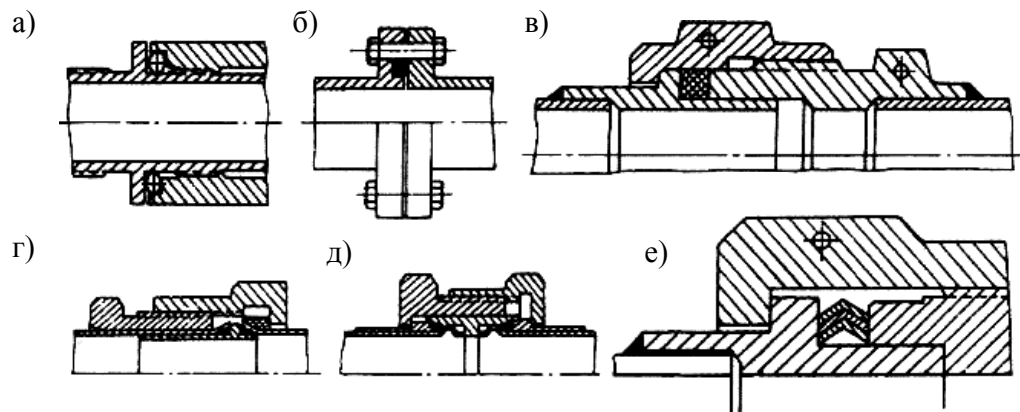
Схемы разъемных неподвижных фланцевых соединений трубопроводов с уплотнительными прокладками: а – с трубчатыми кольцевыми уплотнениями; б – с резиновыми кольцами; в – с прямоугольными гнездами; г, д – с клиновыми гнездами; е – с упругими пластинчатыми элементами
